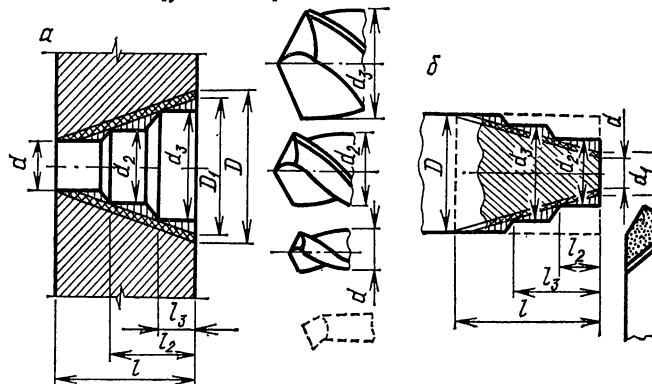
Подготовка заготовок под обработку крутых конусов:
